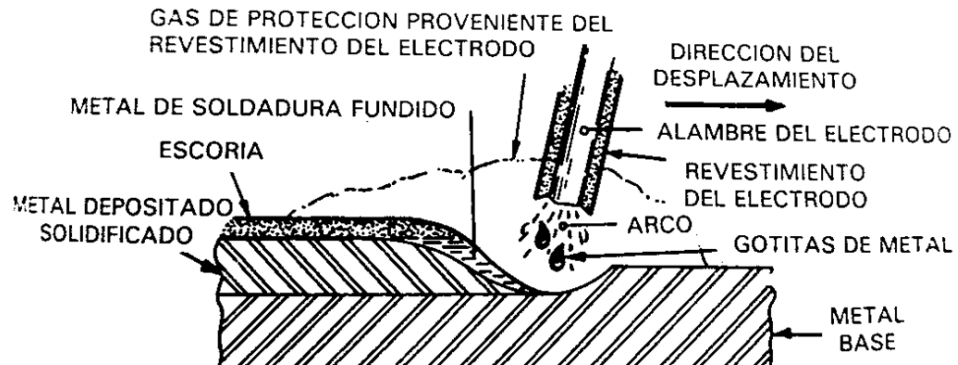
Proceso de soldadura por arco eléctrico con electrodo revestido
